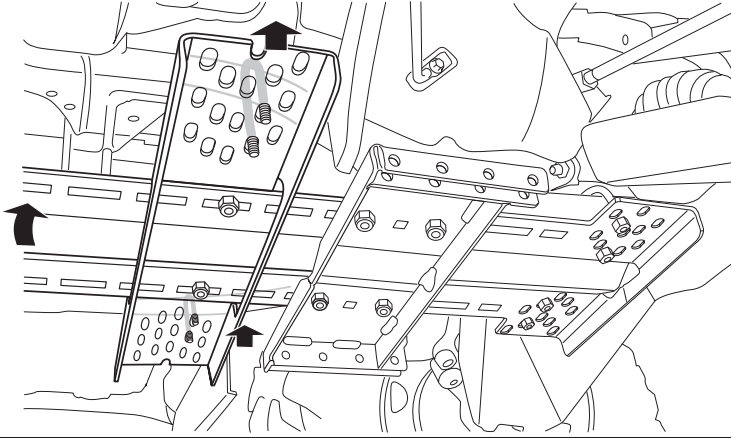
Fixer de manière lâche la plaque de contact arrière aux boulons en U arrière à l'aide des écrous de fixation.
